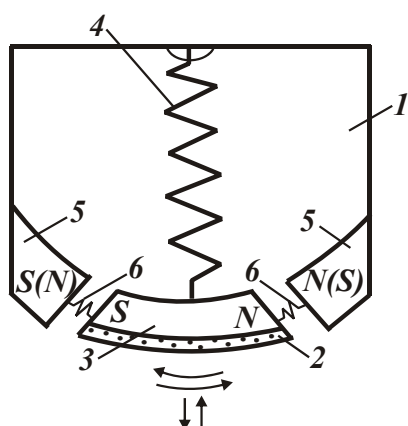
Маятниковая схема электроискрового магнито-импульсного шлифования зубьев, пазов, резьбы, фасок, галтелей выпуклым шлифовальным инструментом: 1 – корпус; 2 – шлифовальный инструмент; 3 – патрон для шлифовального инструмента из магнитных материалов или с электромагнитом; 4 – пружина подвески патрона со шлифовальным инструментом; 5 – управляющие электромагниты; 6 – пружины, отделяющие шлифовальный инструмент от управляющих электромагнитов.
